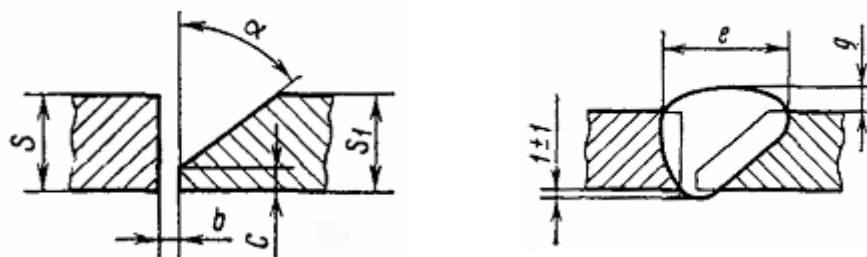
Конструктивные элементы подготовленных кромок свариваемых деталей и шва сварного соединения по ГОСТ 14771-76:
